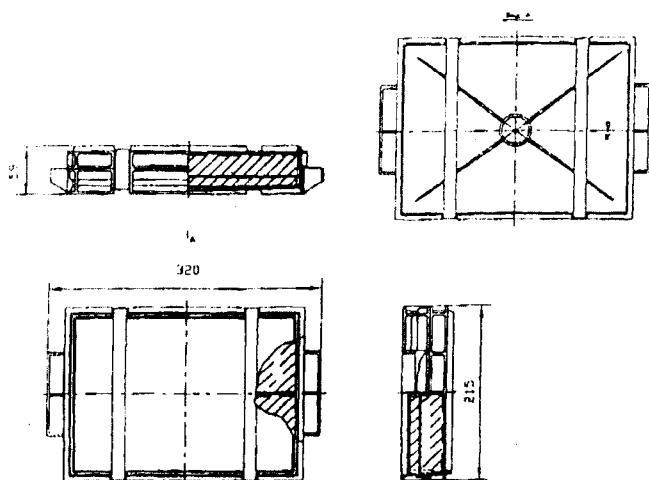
Сборочный чертеж контейнера КТ-6
